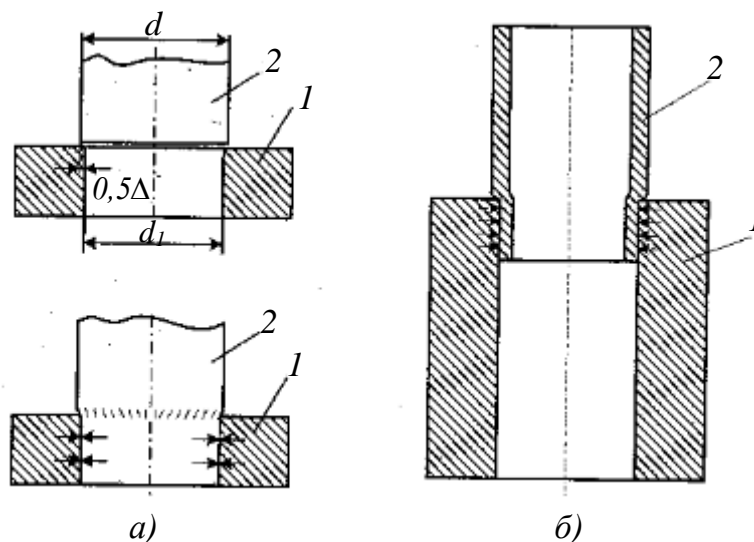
Схемы соединений с нагревом охватывающей или охлаждением охватываемой детали:
